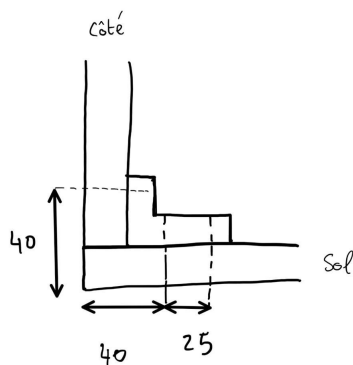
Fixation des plaques de côté à la plaque du sol
